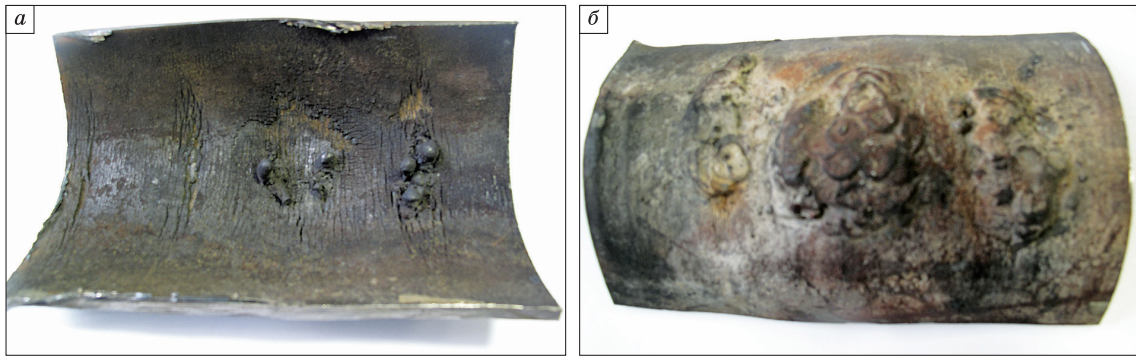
Внешний вид образца трубы поддува после ремонтной сварки:
